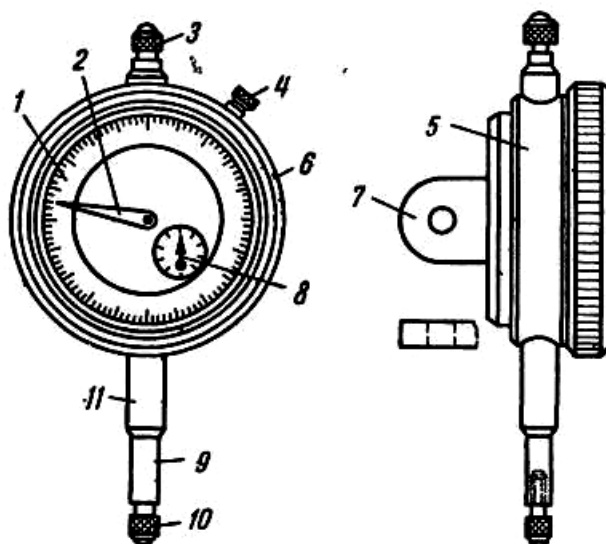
Индикатор часового типа: 1 – большая шкала; 2 – стрелка; 3 – головка измерительного стержня; 4 – стопор; 5 – корпус; 6 – ободок; 7 – ушко; 8 – указатель чисел оборотов (целых мм); 9 – измерительный стержень; 10 – наконечник; 11 – гильза
